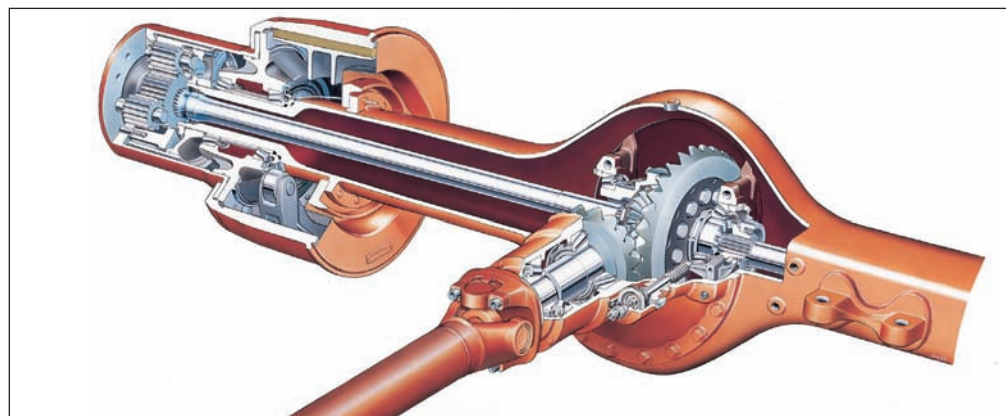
Ведущий мост грузового автомобиля с разнесенной главной передачей и колесными планетарными редукторами
